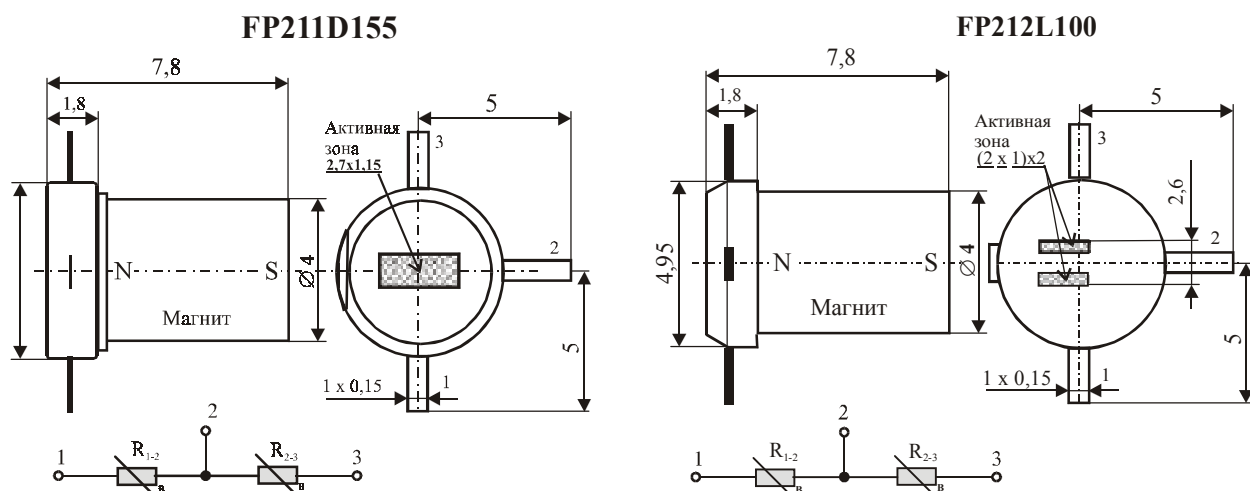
Внешний вид и габаритные размеры магниторезисторов FP 211 D 155, FP 212 L 100
